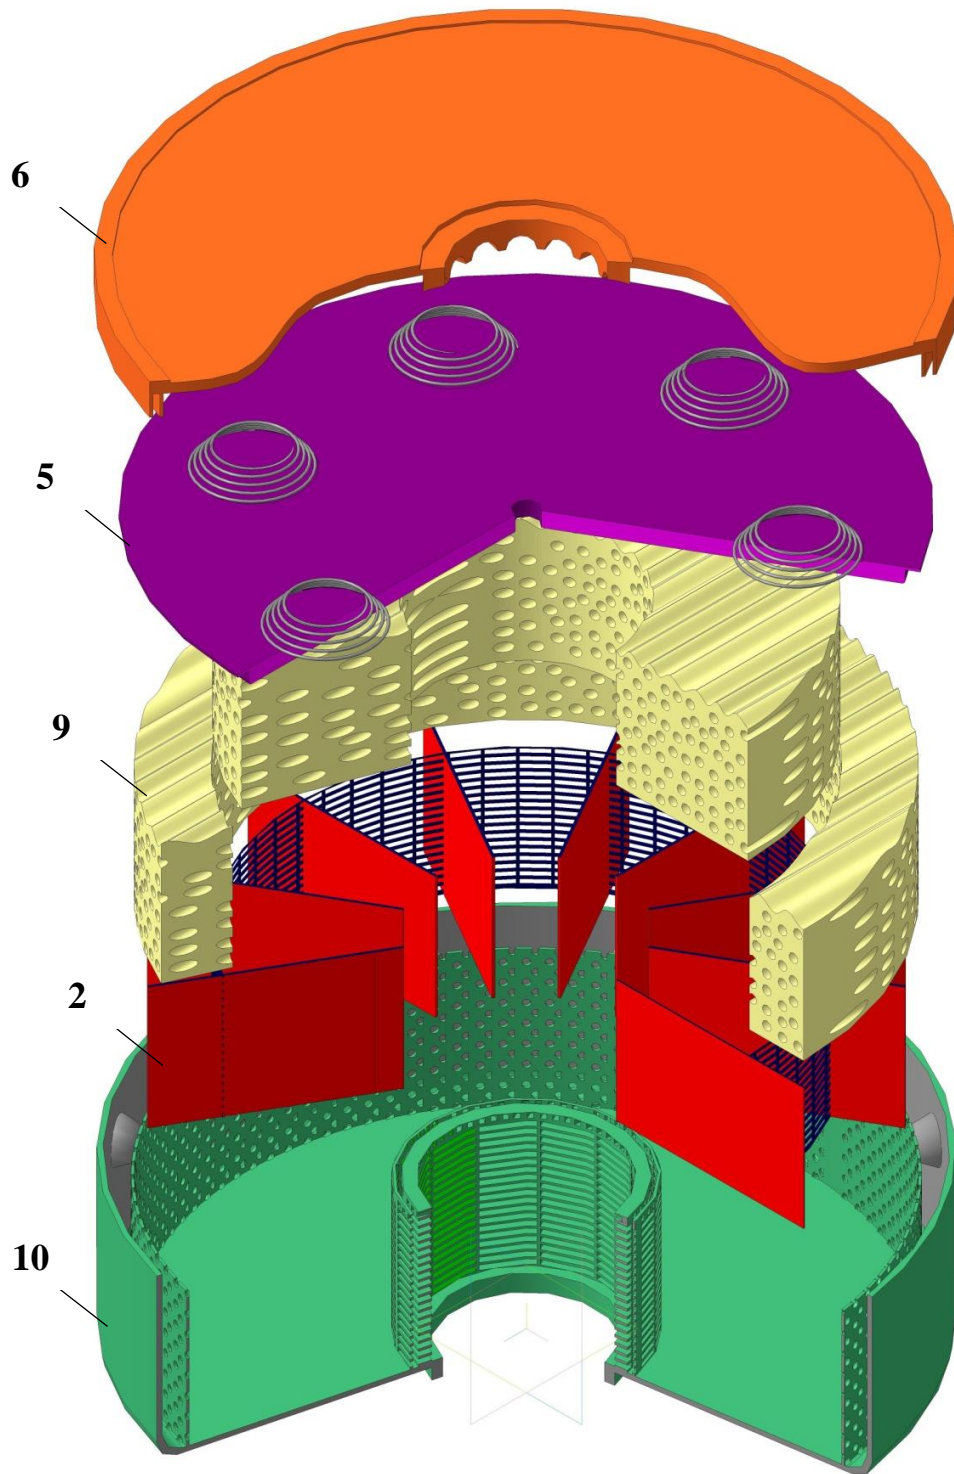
Общий вид регенеративного патрона с центростремительным движением воздуха
